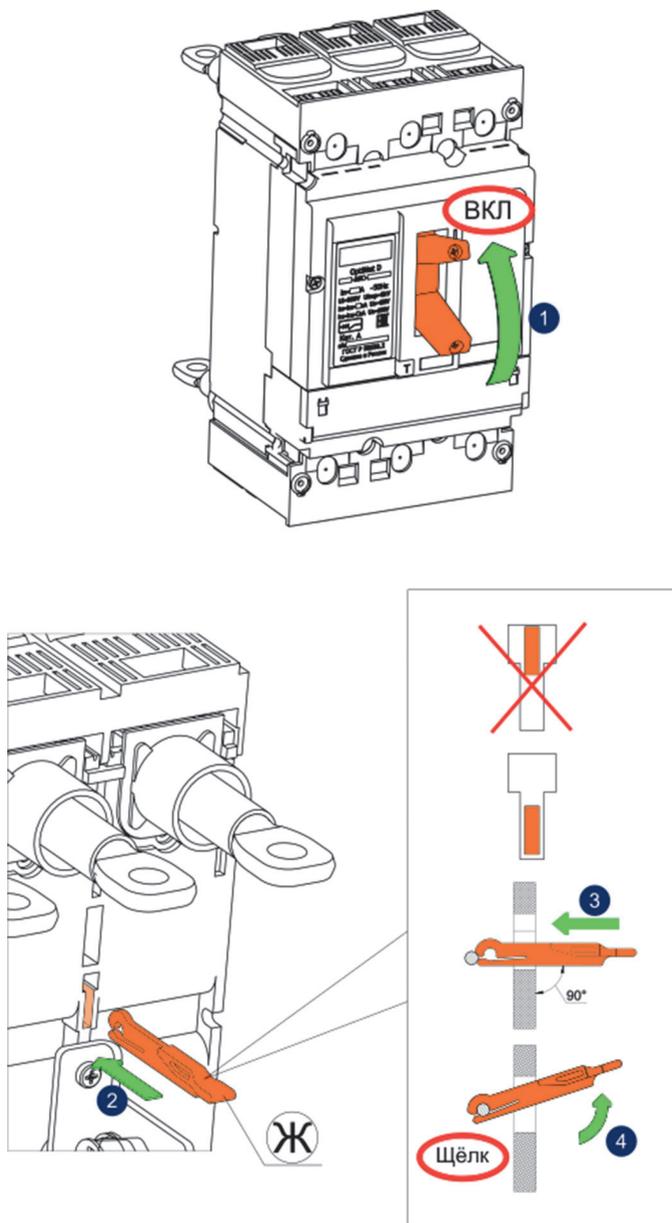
Установка толкателя блокировки на стационарный выключатель
